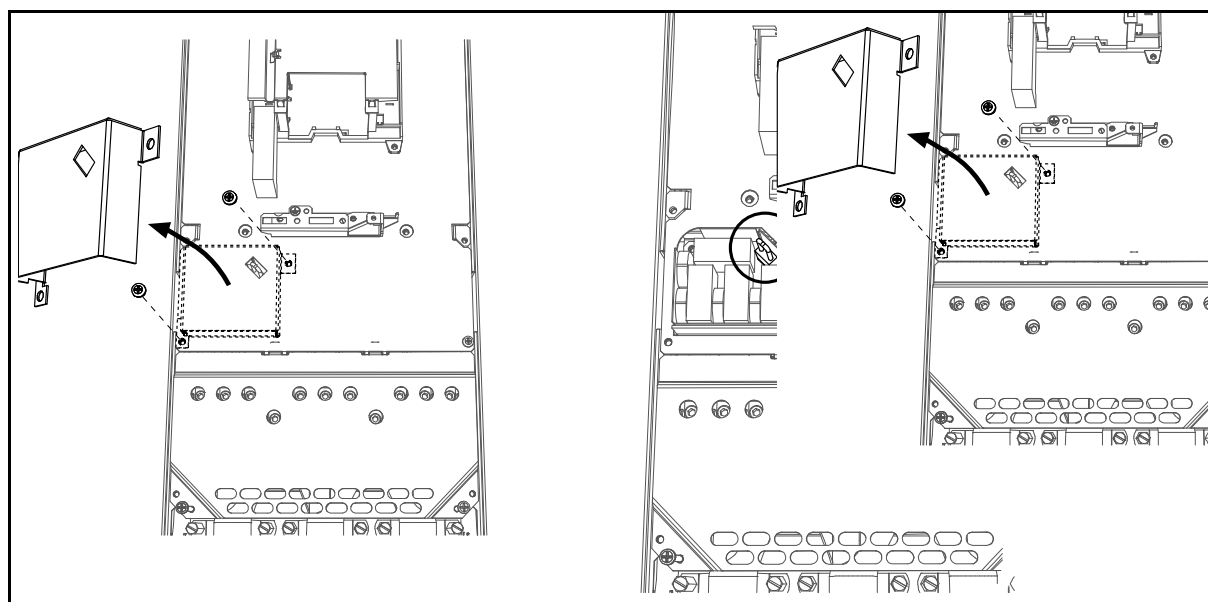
Separación de la conexión tipo puente de EMC, MR7-8
